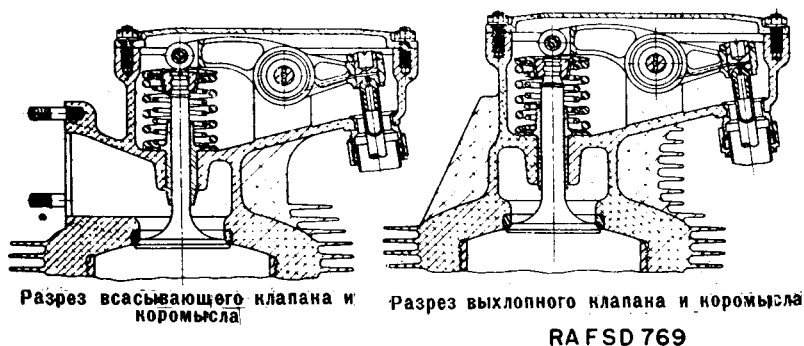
Клапанный механизм радиального дизеля "Гуильберсон".
